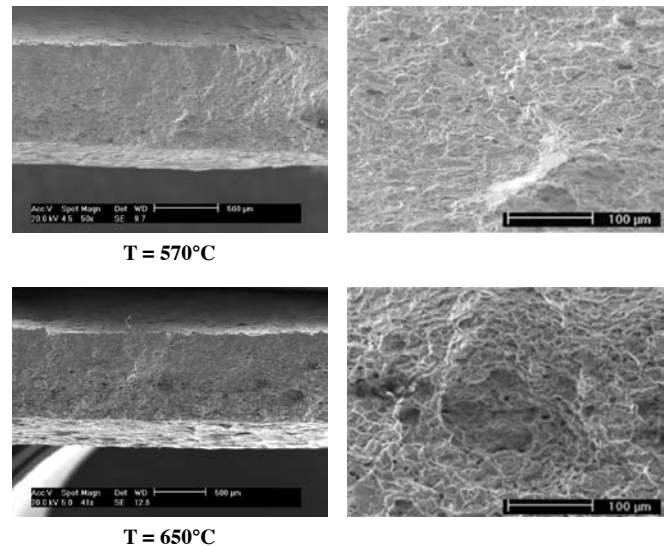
Superficies de fractura de las uniones soldadas de Haynes 230® ensayadas a tracción a altas temperaturas.
